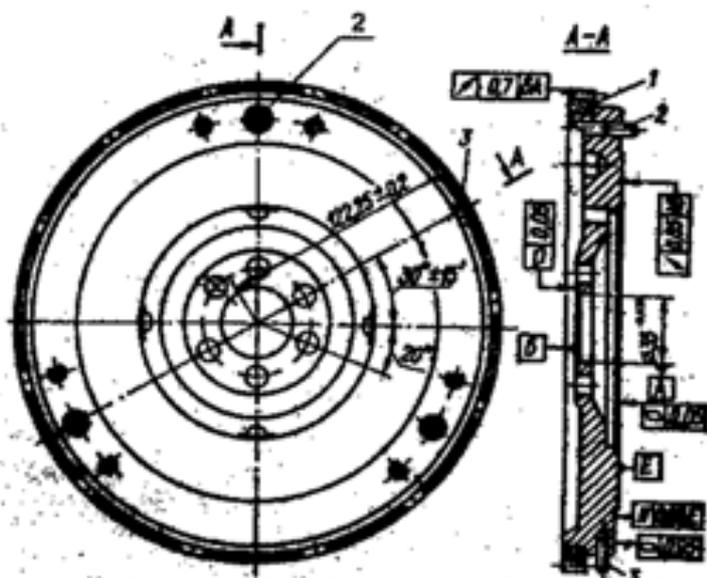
Маховик: 1 - обод маховика; 2 - штифты установки кожуха сцепления; 3 - штифт диагностический ВМТ
